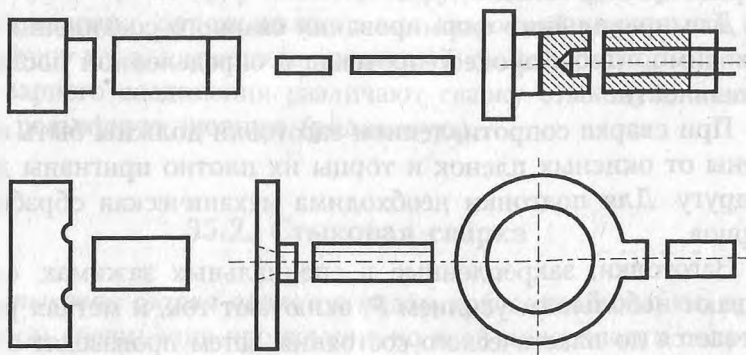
Типы сварных соединений стыковой сварки сопротивлением
